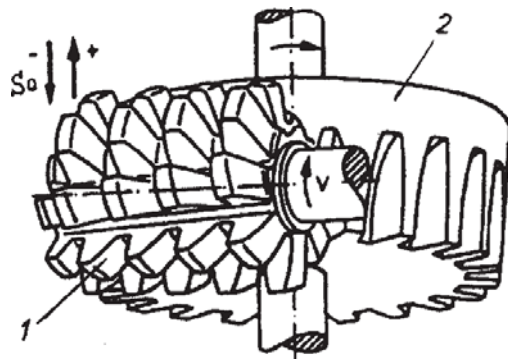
Принцип утворення зубів циліндричних коліс черв'ячною фрезою
